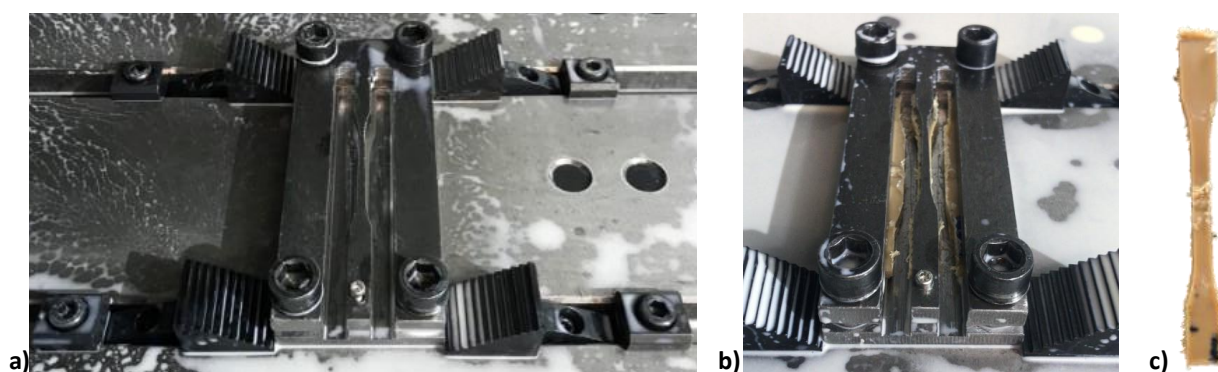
Procedimento para corte de provetes de tração uniaxial: a) Montagem e fixação dos dois módulos da moldura, b) Resultado após procedimento de corte do provete, c) Provette cortado.
